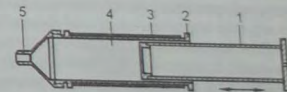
Схема ручного шприца: 1 - поршень; 2 - корпус; 3 - матерчатый шнур; 4 - рабочая полость шприца; 5 - носик шприца
